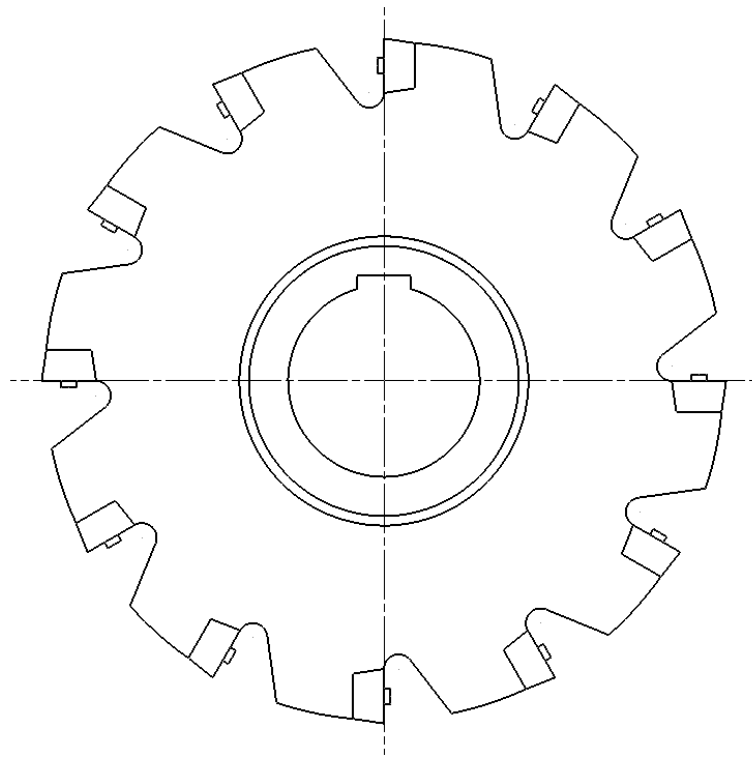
Ескіз конструкції фрези дискової тристоронньої
